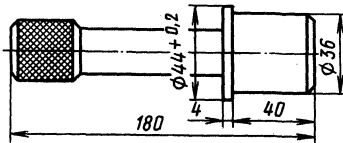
Оправка для запрессовки втулок рычагов передней подвески автомобиля «Запорожец»
